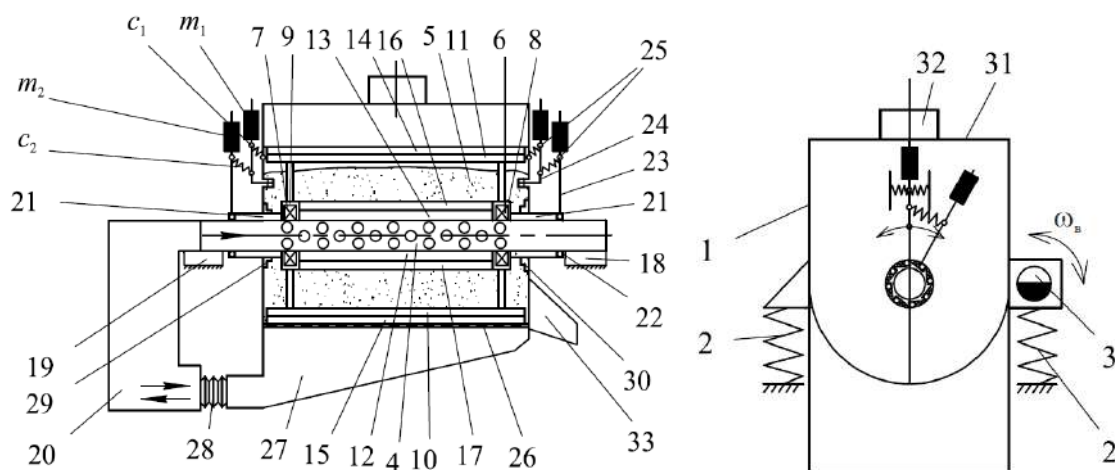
Віброозонуюча сушарка з перемішувачами і маятниковими механізмами вільного ходу: 1 – камера U-подібної форми; 2 – пружини; 3 – віброзбуджувач; 4 – газорозподільна решітка; 5 – зернова сировина; 6, 7 – корпуси підшипників; 8, 9 – підшипники; 10-13 – лопаті-перемішувачі; 14-17 – еластичні скребки; 18, 19 – опори; 20 – система подачі-відбору сушильного агента; 21 – втулка; 22 – маятникові механізми; 23, 24 – маятники; 25 – пружини; 26 – перфороване днище; 27 – дифузор; 28 – еластичне з'єднання; 29, 30 – пружні вставки; 32 – завантажувальний отвір; 33 – розвантажувальний лоток
